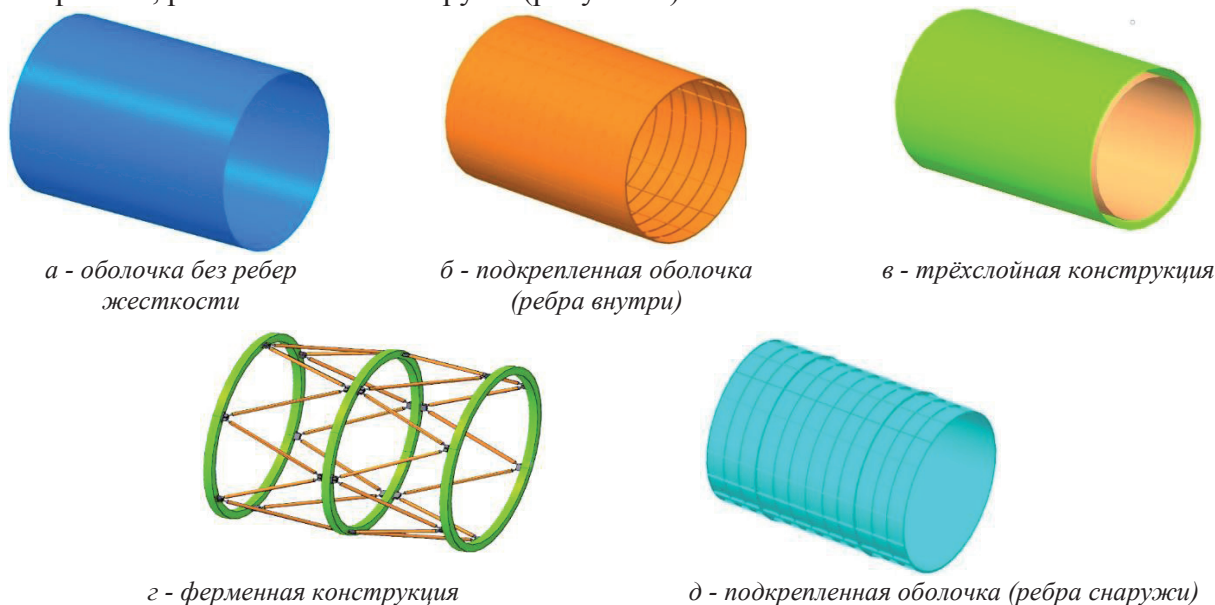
Варианты конструктивного исполнения корпусной конструкции
